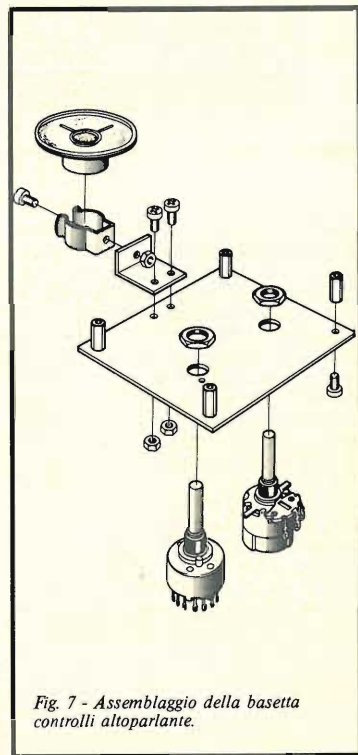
Assemblaggio della basetta controlli altoparlante.
